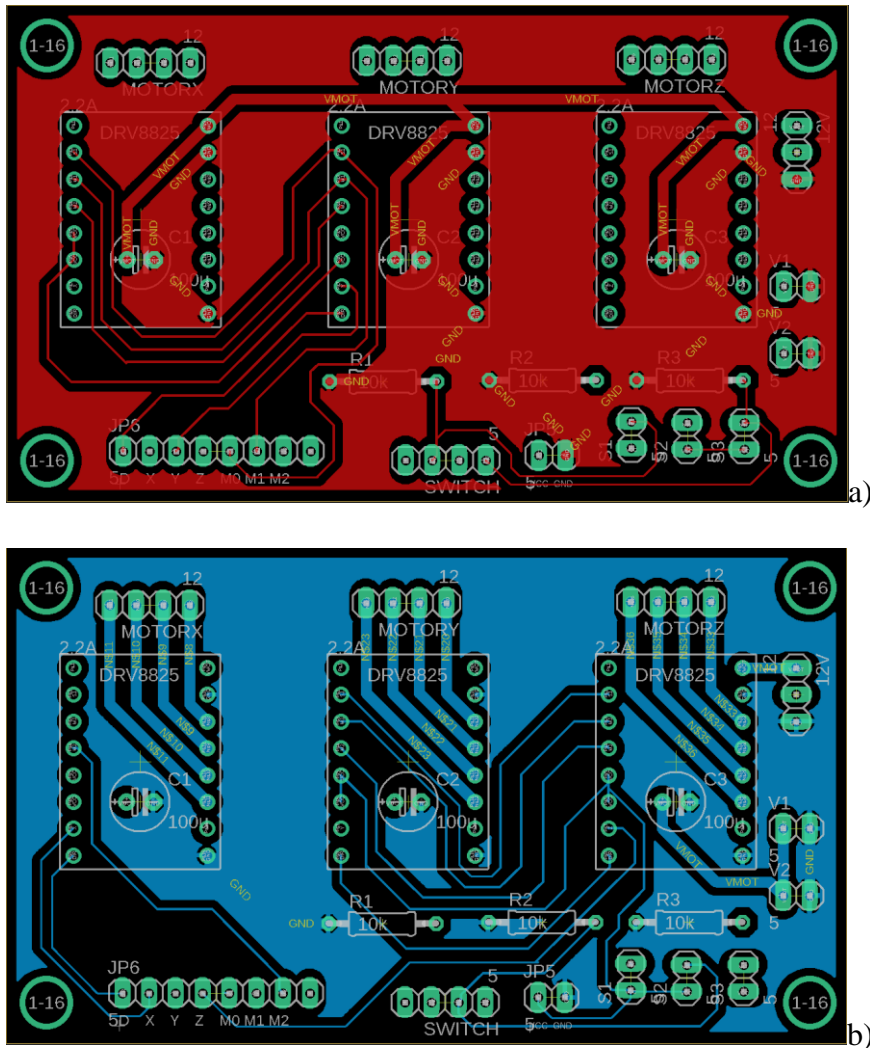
Diseño de PCB. Capa TOP (a), Capa BOTTOM (b)
